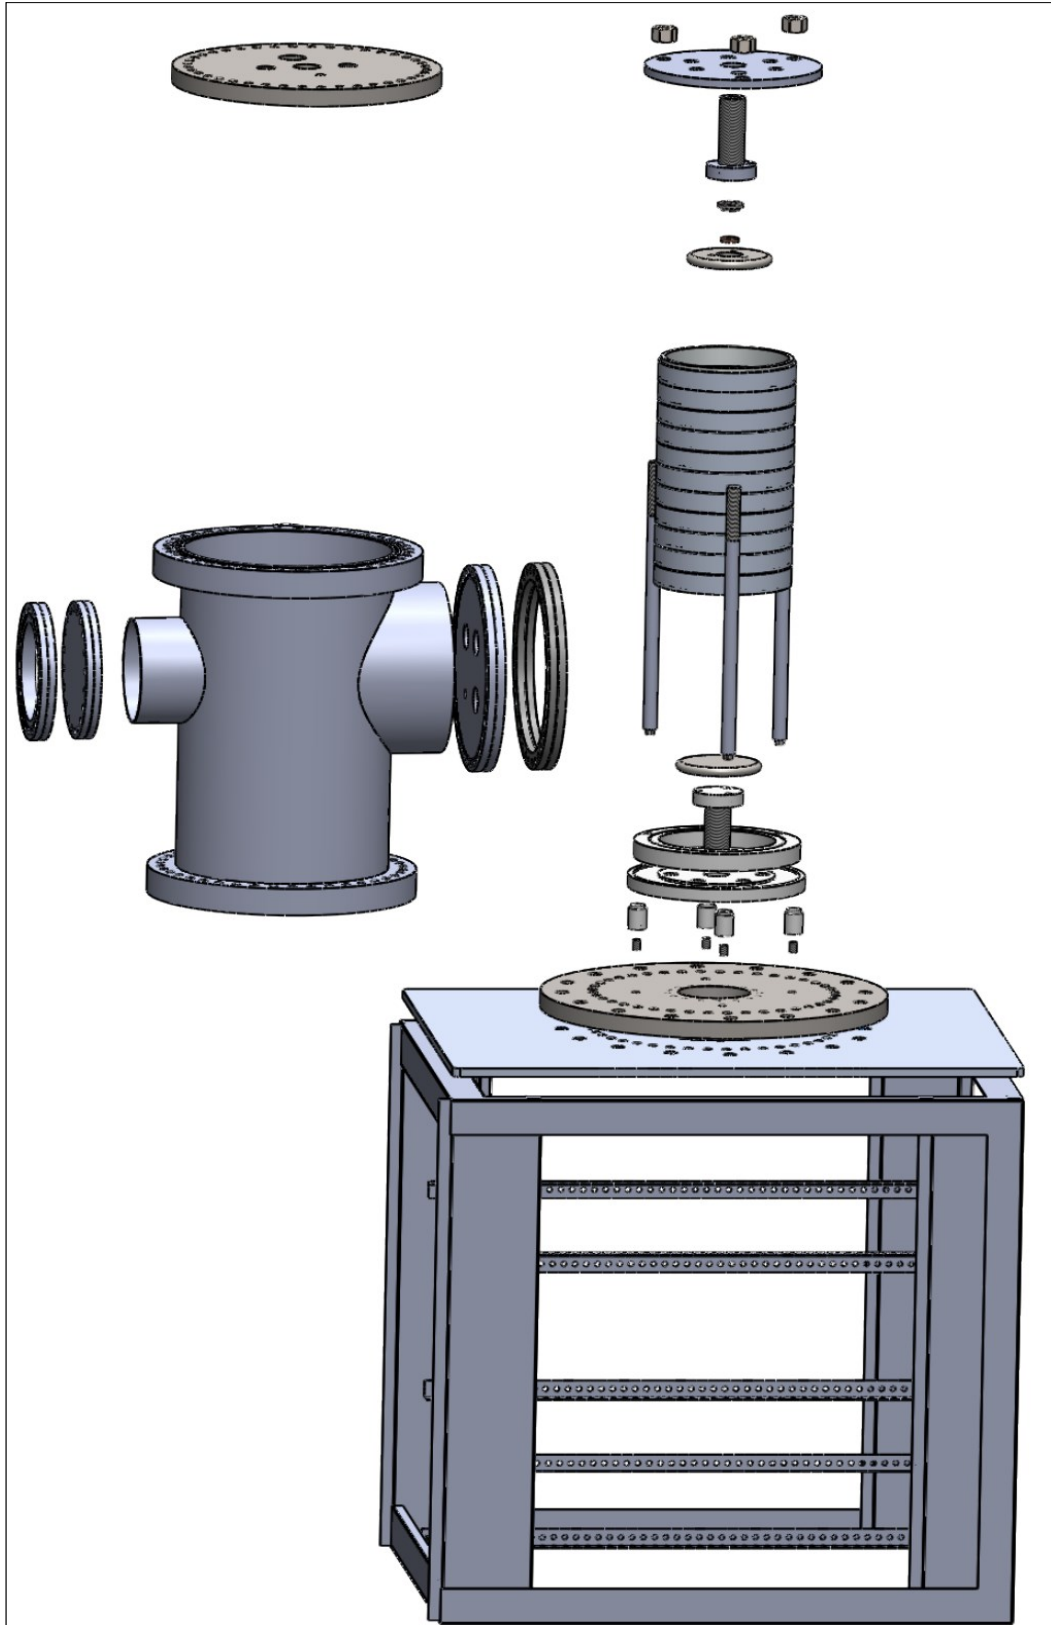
Vista explosionada del ensamblaje de la cámara de Townsend
